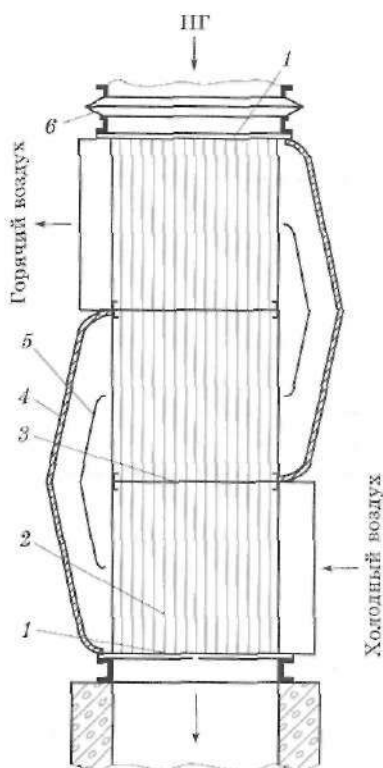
Рекуперативный стальной трубчатый воздухоподогреватель:
